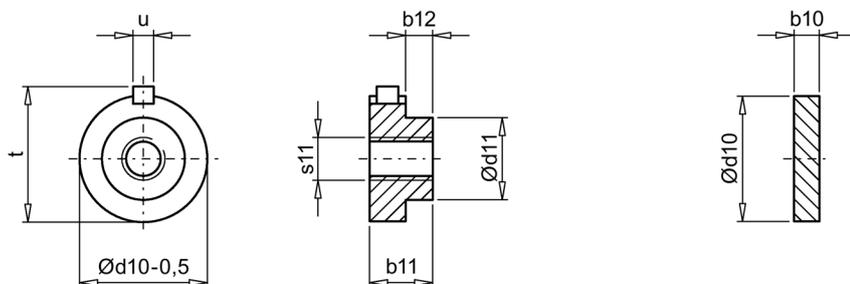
Демонтаж полого вала с призматической шпонкой
